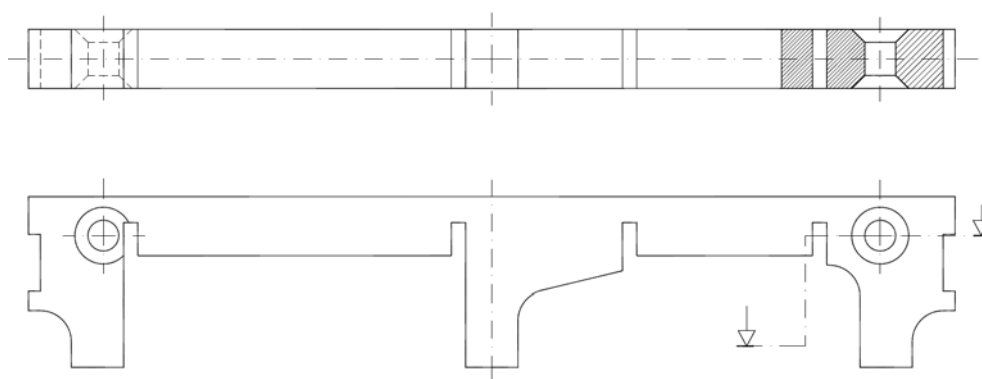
Zapata modificada fijada al pistón de compresión y empuje del bloque en el molde de la máquina-prensa.
